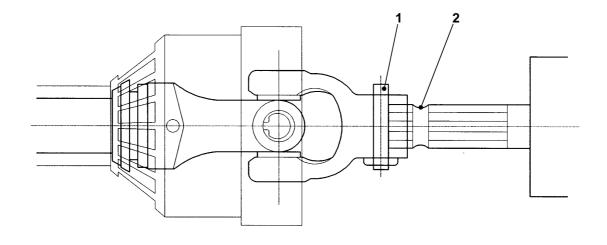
Collegamento albero cardanico - Cardan shaft connection
